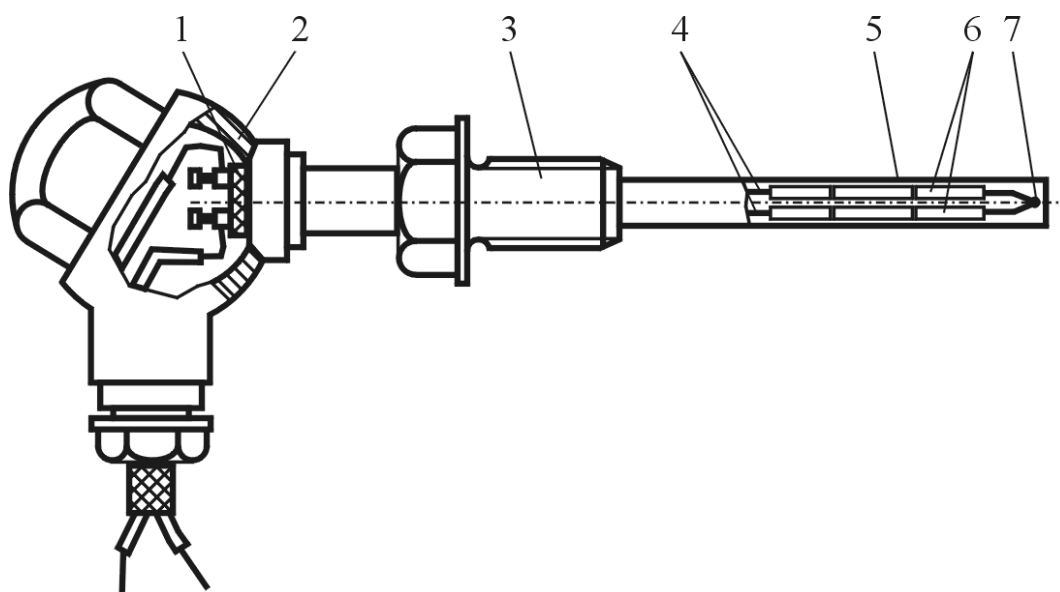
Технічний термоелектричний термометр: 1 – клемна колодка; 2 – корпус; 3 – штуцер; 4 – термоелектроди; 5 – захисний чохол; 6 – фарфорові трубки; 7 – робочий спай
